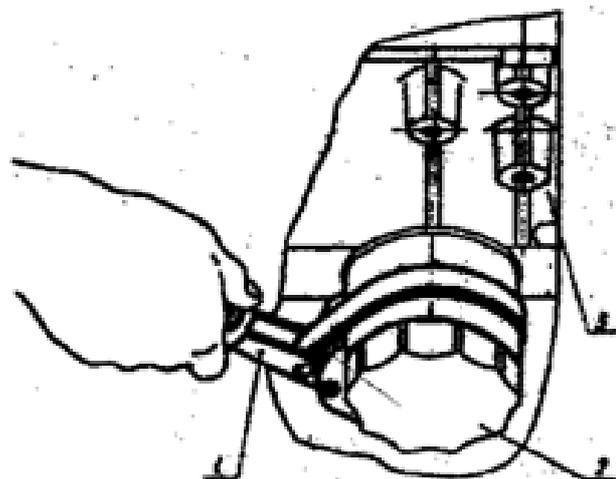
Снятие масляного фильтра: 1-приспособление; 2-масляный фильтр; 3-картер двигателя
